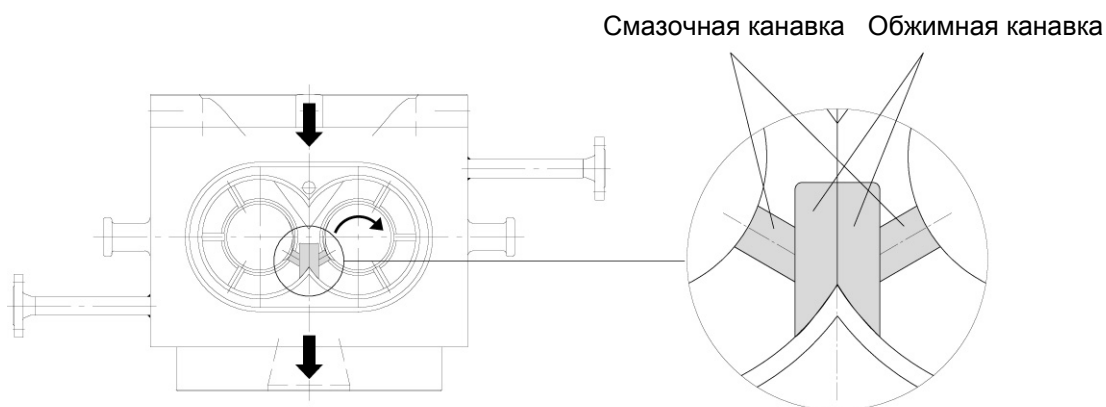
Вид с приводной стороны в корпус на подшипники неприводной стороны
